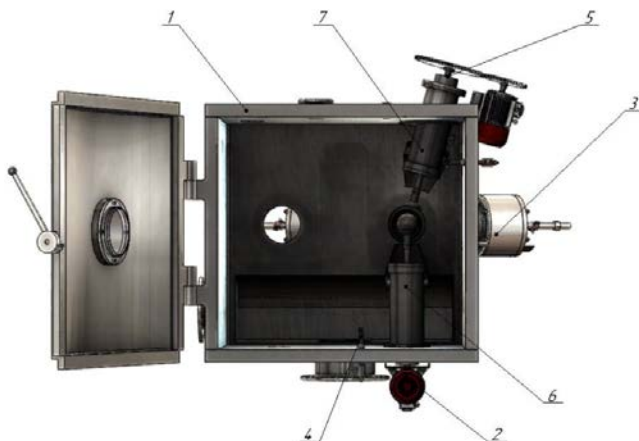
Общий вид установки для напыления вакуумных покрытий на сферические поверхности
